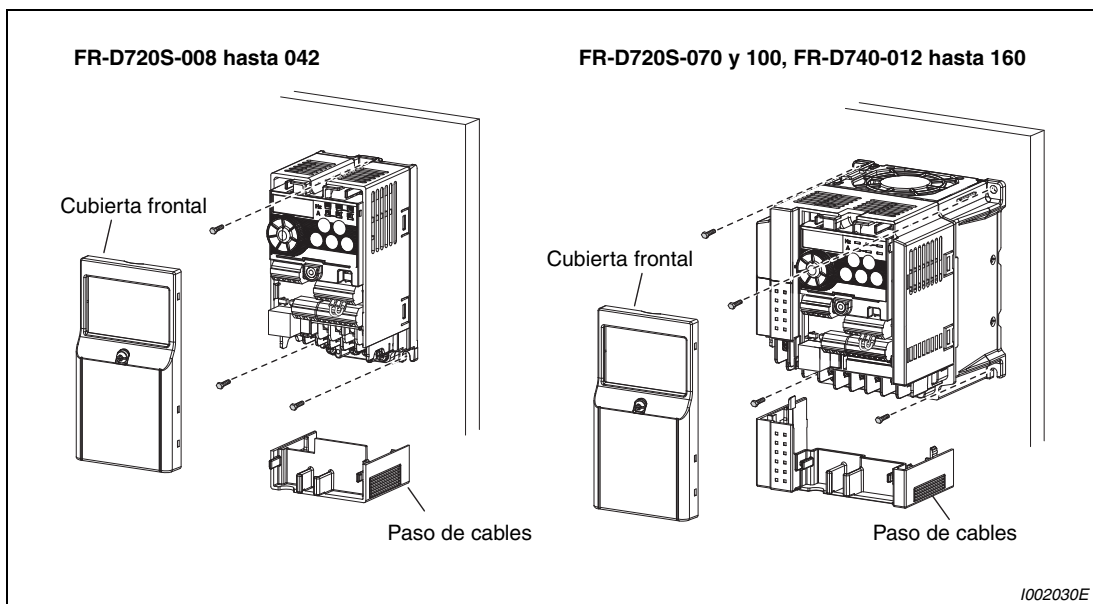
Instalación sobre la placa de montaje de un armario de distribución
